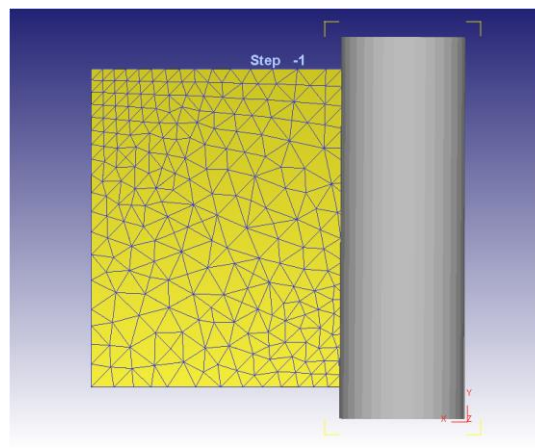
Позиціонування інструменту відносно заготовки (вид зверху)
